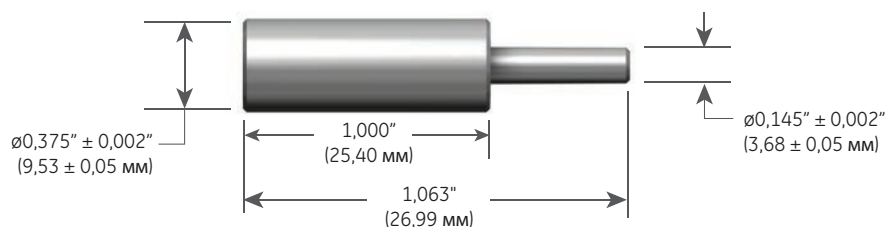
Инструмент для установки верхнего уплотнения регулятора
